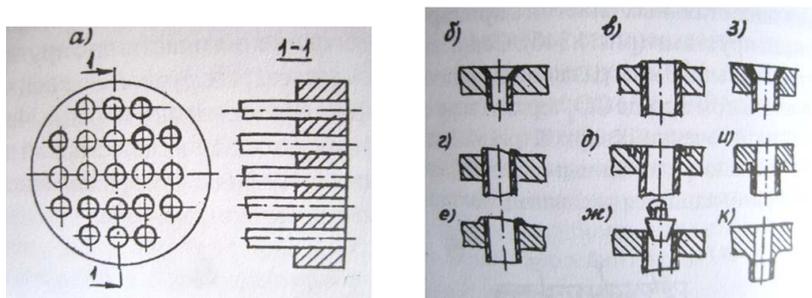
Соединение труб с трубными досками: а – схема размещения труб с доской; б, в, г, д, е, ж, з – формы подготовки кромок труб
